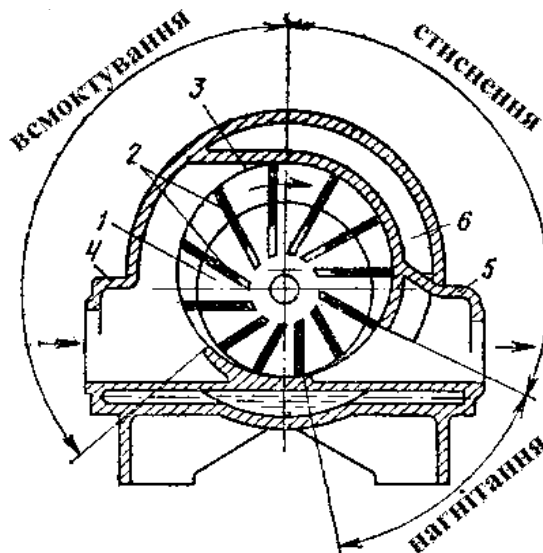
Схема ротаційно–пластинчатого компресора:
